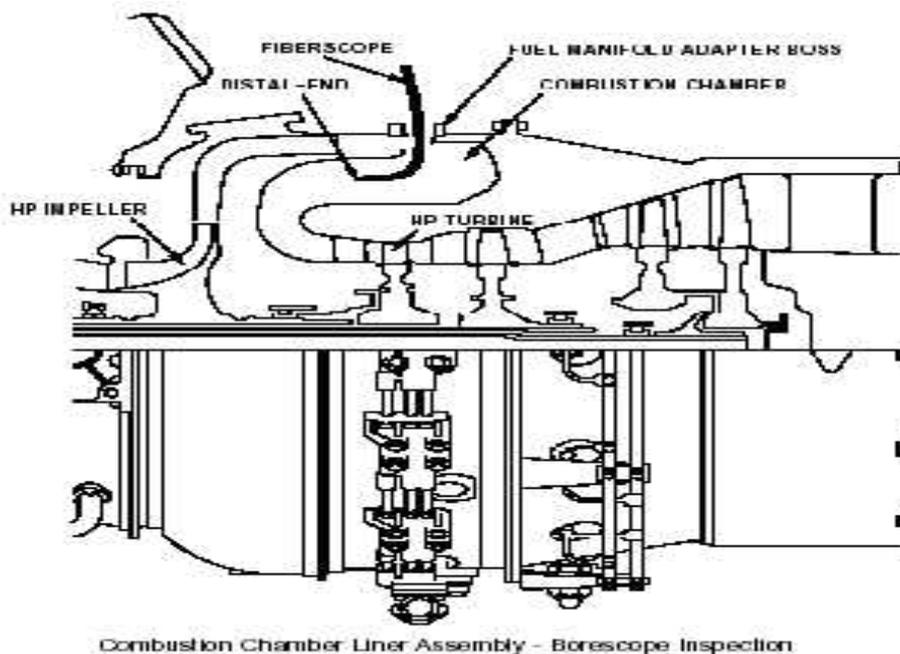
Inspection d'assemblage enveloppe de la chambre de Combustion.
